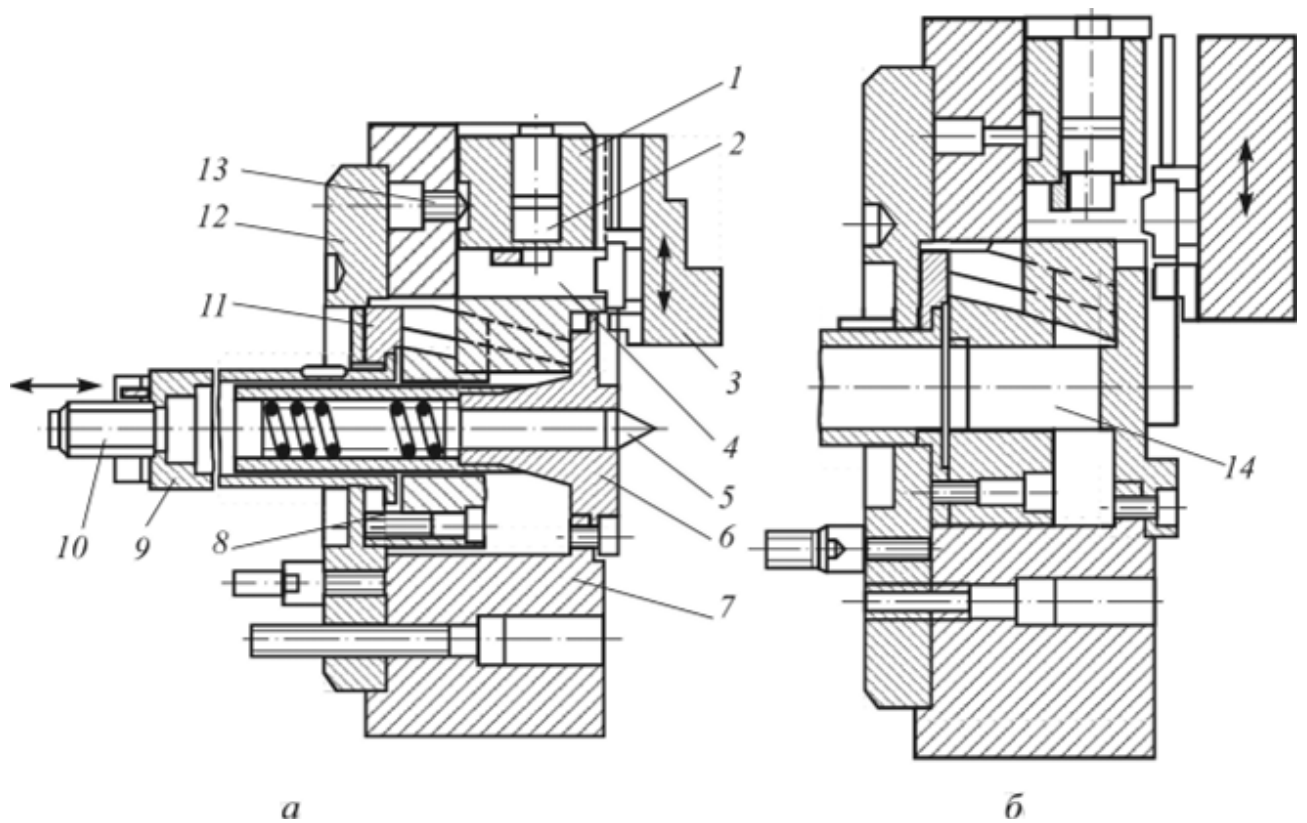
Самоцентруючі трикулачкові клинові патрони для обробки заготовок типу вал (а) та диск (б)
